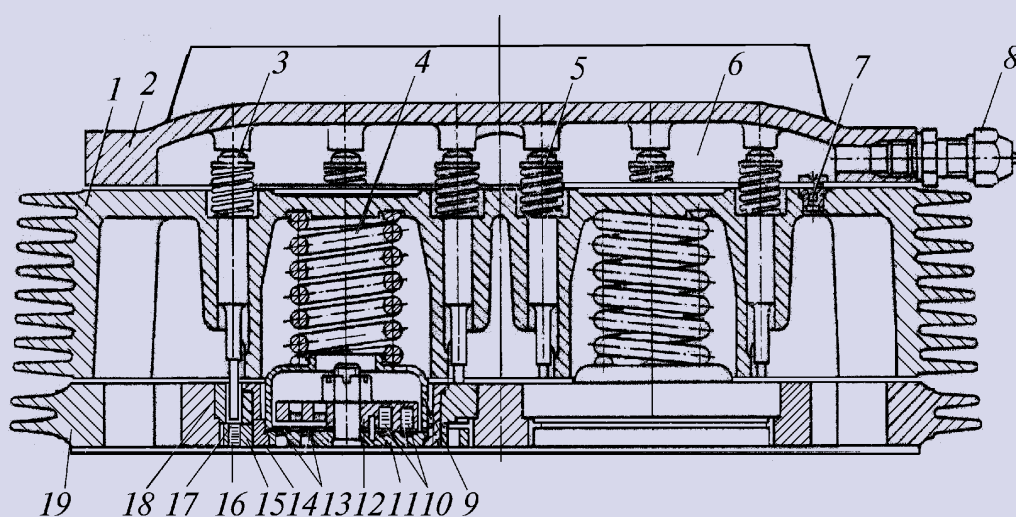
Клапанная плита в головке цилиндров компрессора типа «V»: 1 — головка цилиндров; 2 — крышка цилиндров; 3 — штифт; 4 — буферная пружина; 5, 10, 16 — пружины; 6 — торцевая крышка; 7 — сопло; 8 — штуцер; 9 — упорный стакан; 11 — гнездо нагнетательного клапана нижнее; 12 — гнездо нагнетательного клапана верхнее; 13, 17 — пластины; 14 — соединительный стакан; 15 — нижнее гнездо; 18 — верхнее гнездо; 19 — клапанная плита
